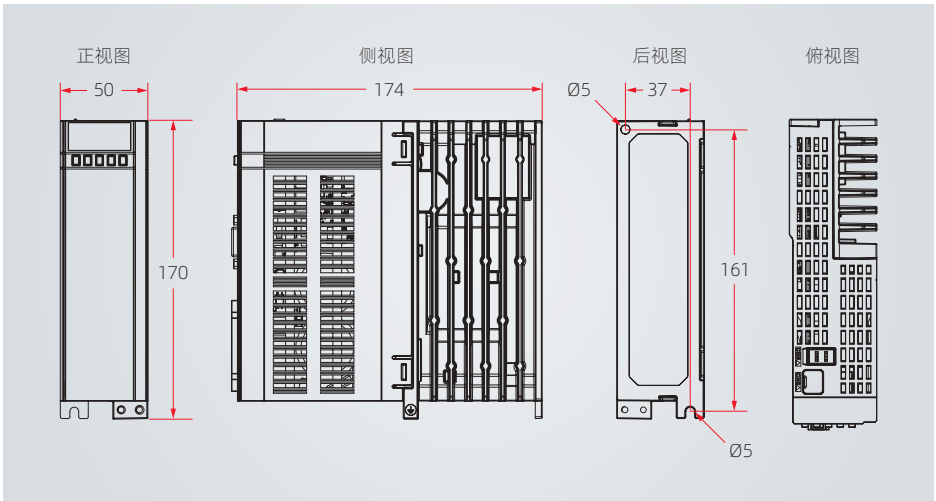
驱动器 (SIZE B) 安装尺寸示意图 (单位: mm)
